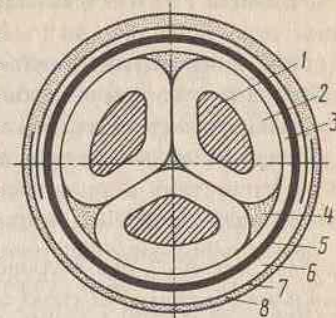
Эскиз поперечного сечения кабеля с поясной изоляцией:
